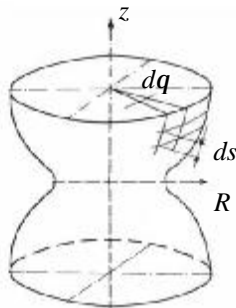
Схема разбиения заготовки на участки в цилиндрической системе координат
